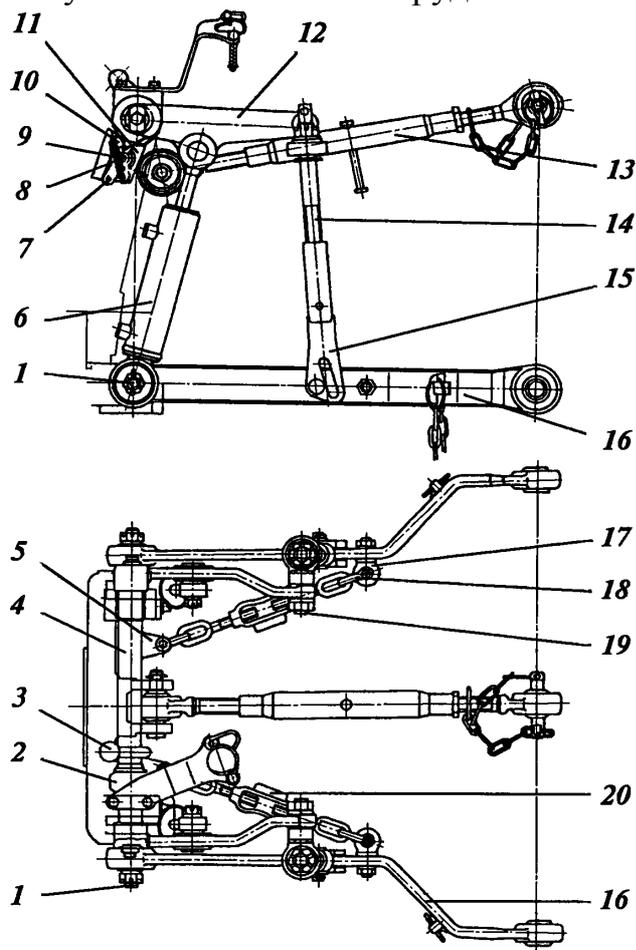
Навесное устройство: 1 - ось продольных тяг; 2 - упор; 3 - рукоятка; 4 - поворотный вал; 5, 7, 10, 11 - кронштейны; 6 -
